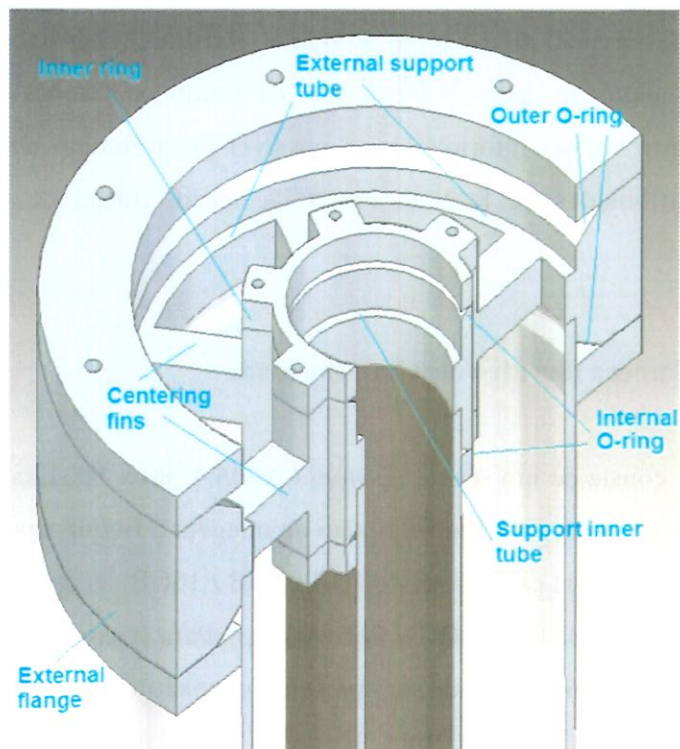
Corte transversal e detalhe do flange Superior com seus anéis.
